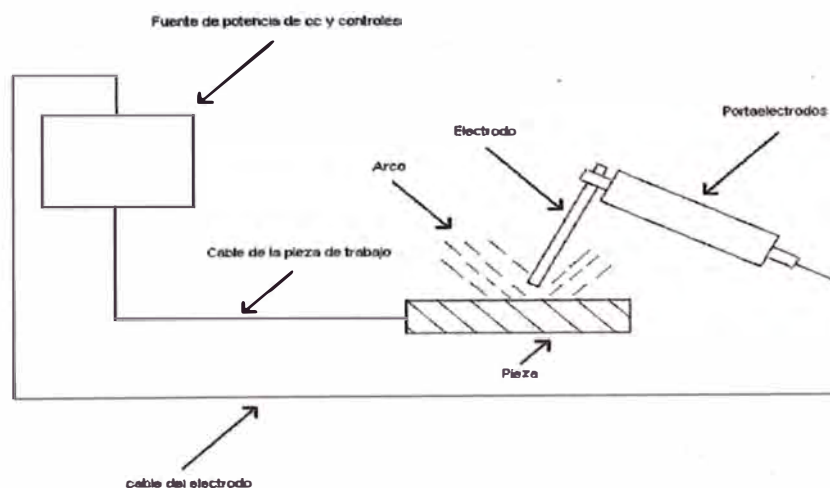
Elementos de un circuito de soldadura típico para soldadura de metal protegido
